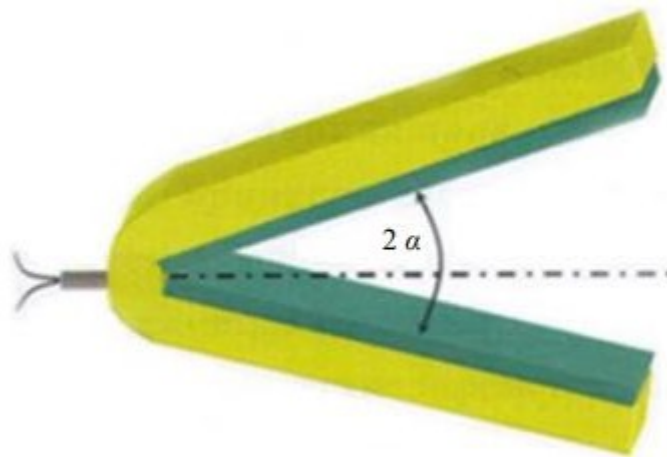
Симетрична схема зварювання вибухом плоских заготовок
